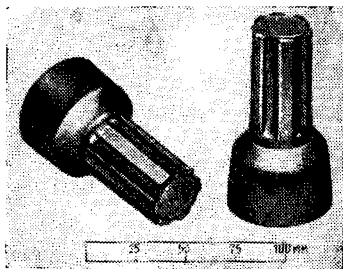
Поковка промежуточного вала для автомобиля, изготовленная из углеродистой стали (заготовка диаметром 60 мм, длиной 49 мм. нагрев 1065° С)
